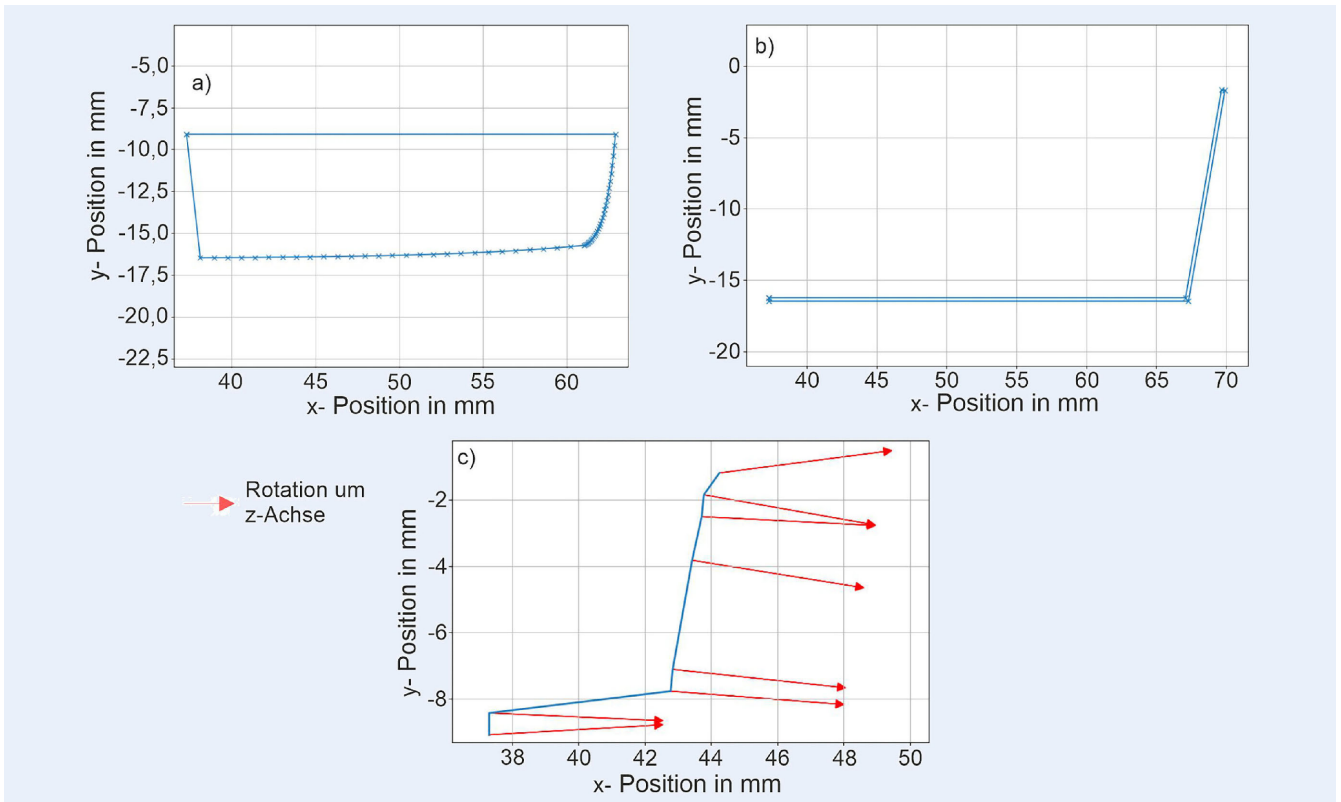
Übersicht über die Werkzeuggeometrie und Profilgeometrie: a) Oberwerkzeuggeometrie, b) Hutprofil, c) Werkzeugbahn. Grafik: IFUM Hannover
